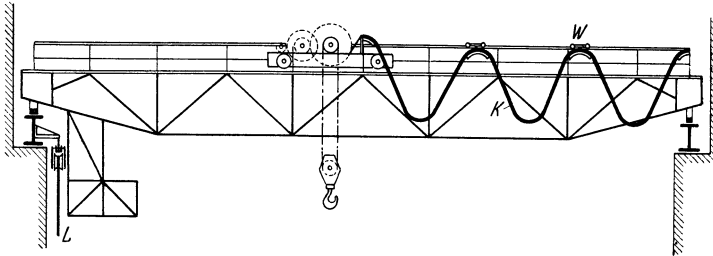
Laufkran-Stromzuführung in einem explosionsgefährdeten Raum.
